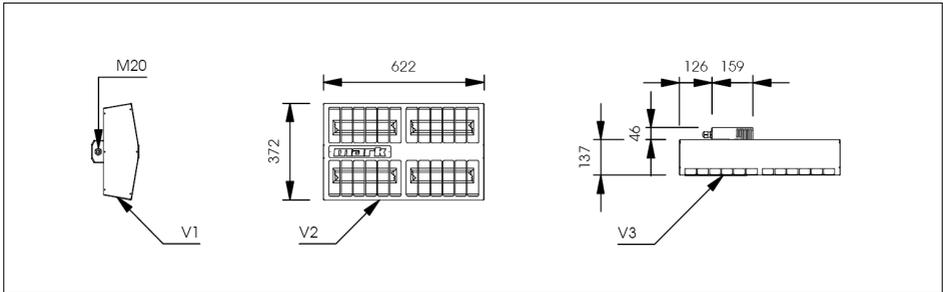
Dimensions du INFRA ER 3200. (V1 : Vue latérale gauche, V2 : Vue de dessous, V3 : Vue de face)
